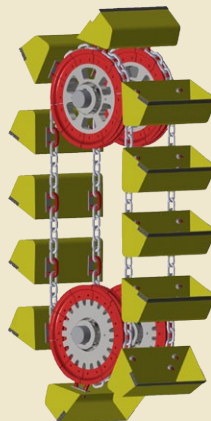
Ковшовый элеватор с гладкими приводными колесами
